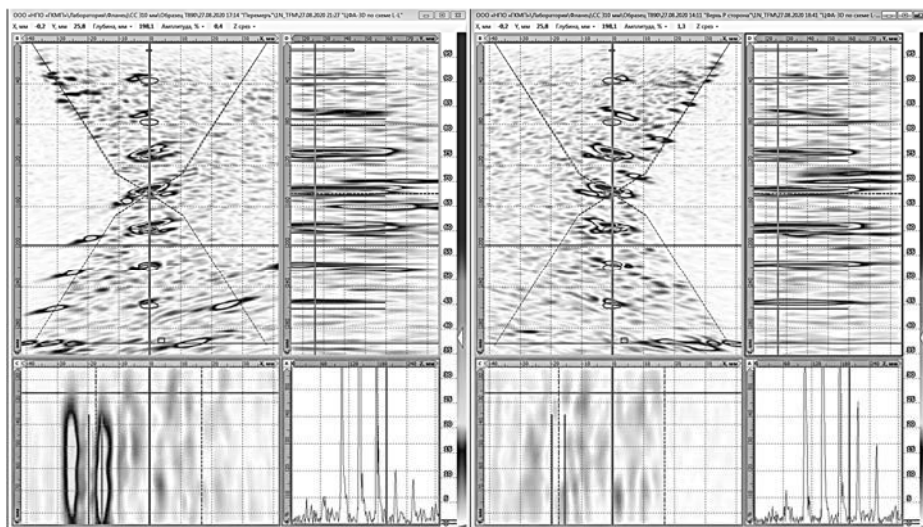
Выявление БЦО на оси сварного шва в настроечном образце при контроле с двух сторон от сварного шва
